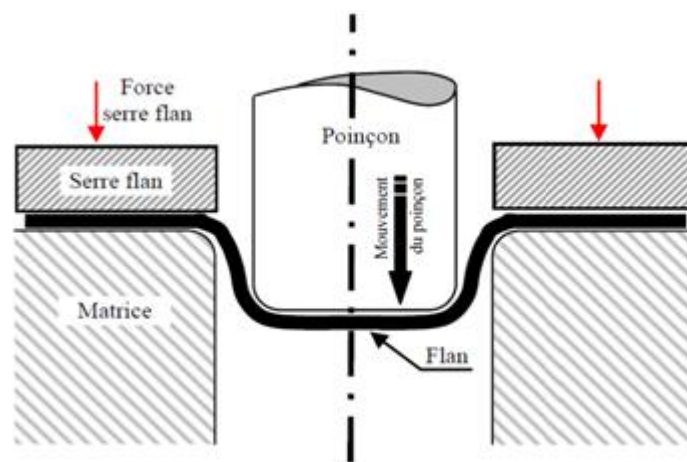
Procédé d'emboutissage avec freinage de la tôle sous serre flan.
